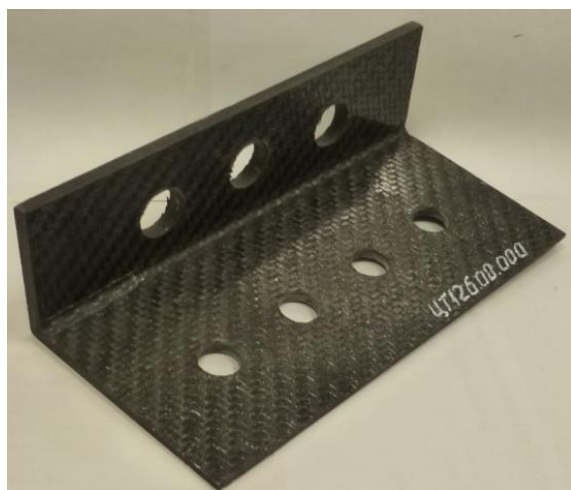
Внешний вид конструктивно-подобного элемента фланцевого соединения
